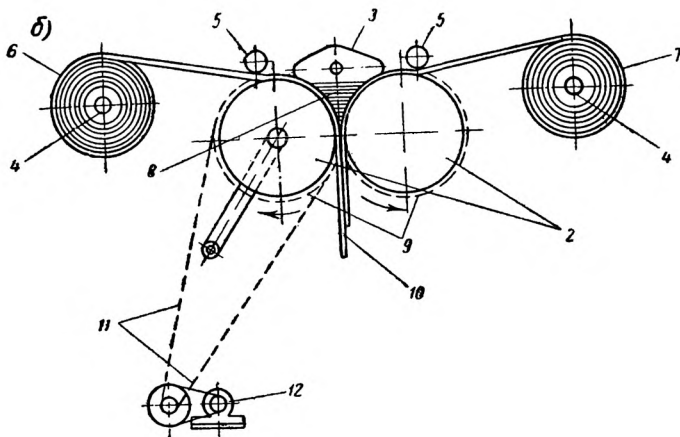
Станок ДРМ-1 для изготовления двухслойных материалов:
